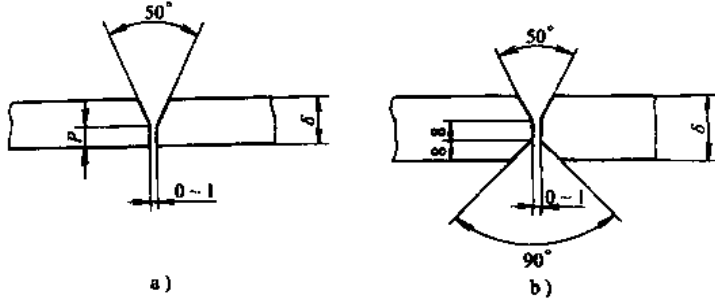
单丝双面埋弧焊对接坡口形式
